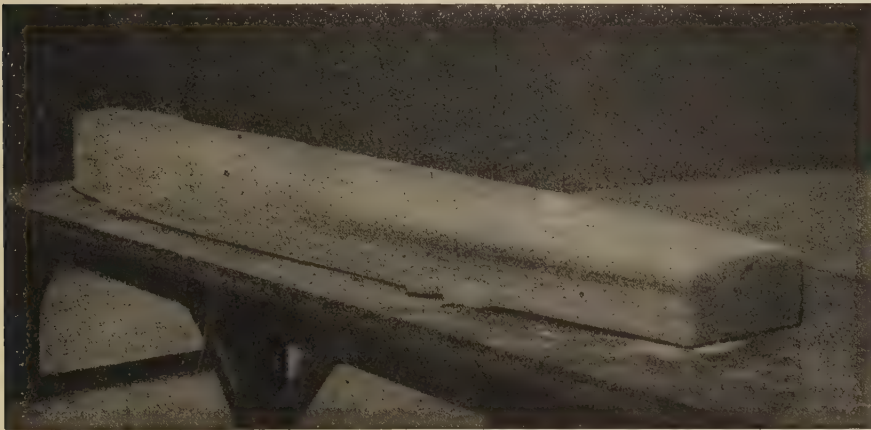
Fertig gefrästes Schiffmodell vor seiner endgültigen Bearbeitung auf die gewünschte Form.
